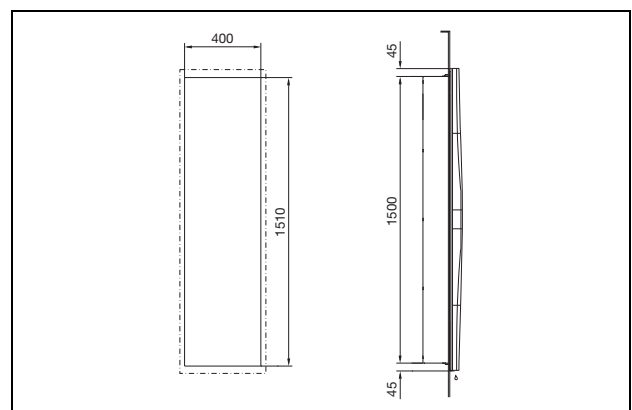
SK 3303.xxx, SK 3361.xxx vnitřní montáž
